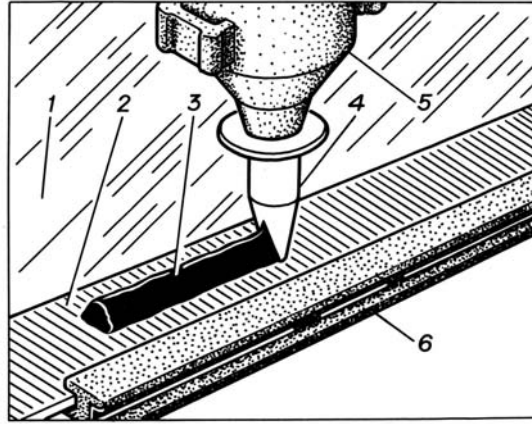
Нанесение клея: 1 – стекло; 2 – праймер; 3 – клей; 4 – насадка; 5 – приспособление для выдавливания клея; 6 - уплотнитель
